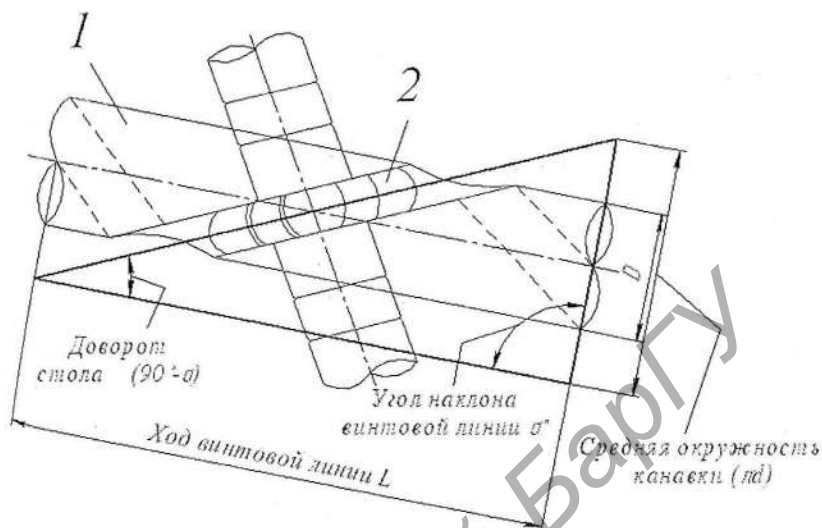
Доворот (смещение) стола фрезерного станка:
